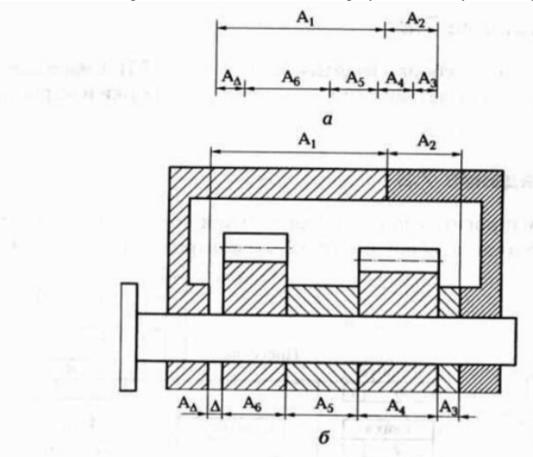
Линейная технологическая размерная цепь: а — схема сборочной размерной цепи; б — сборочный чертеж
